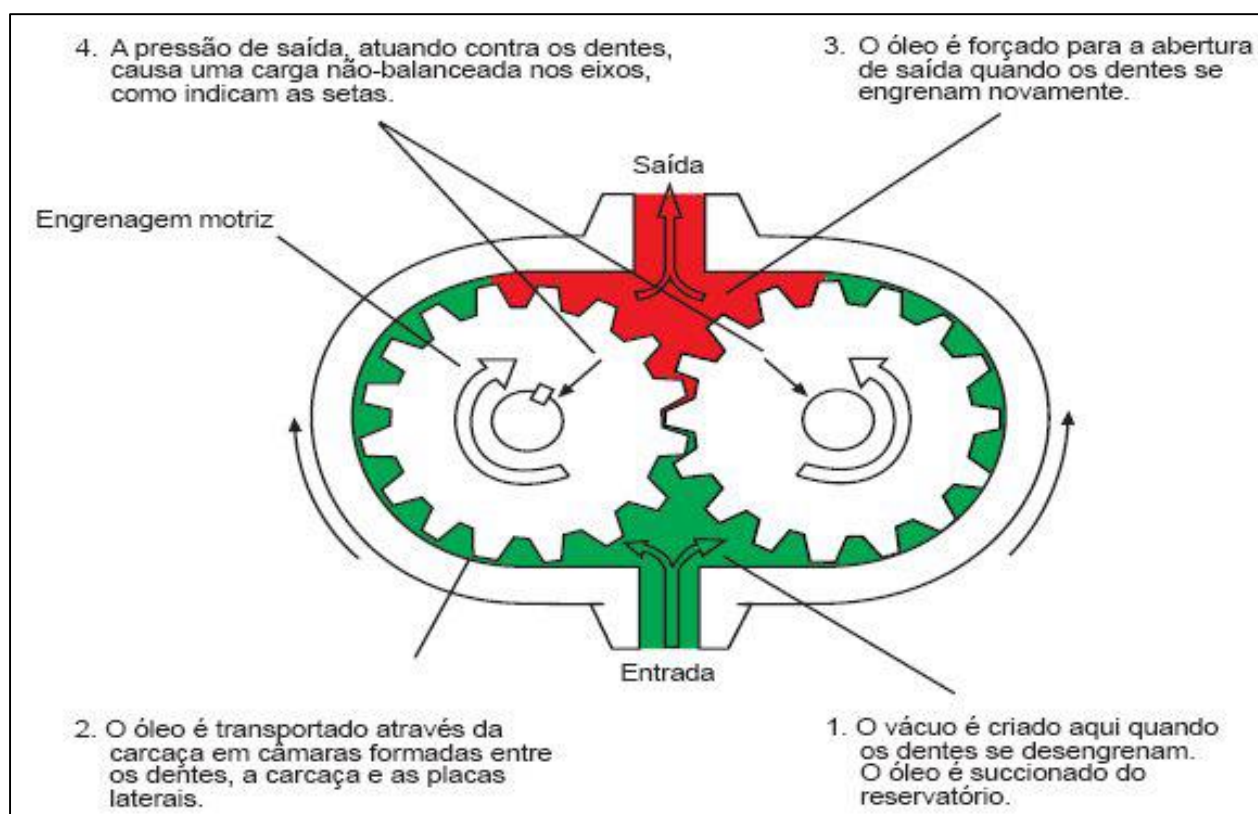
Exemplo de uma bomba de engrenagem externa.
